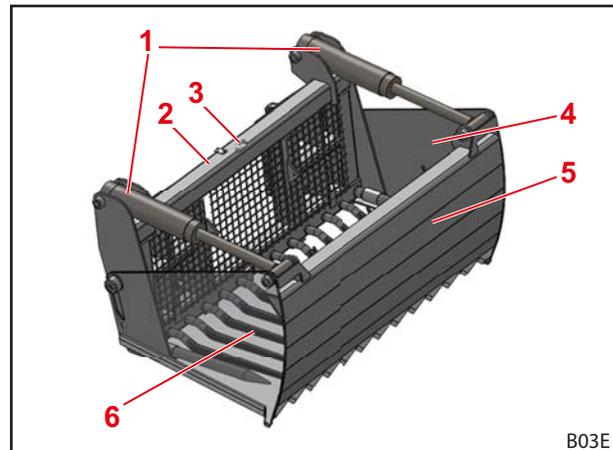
Aufbau Silageschneidzange mit 2 Hydraulikzylindern
